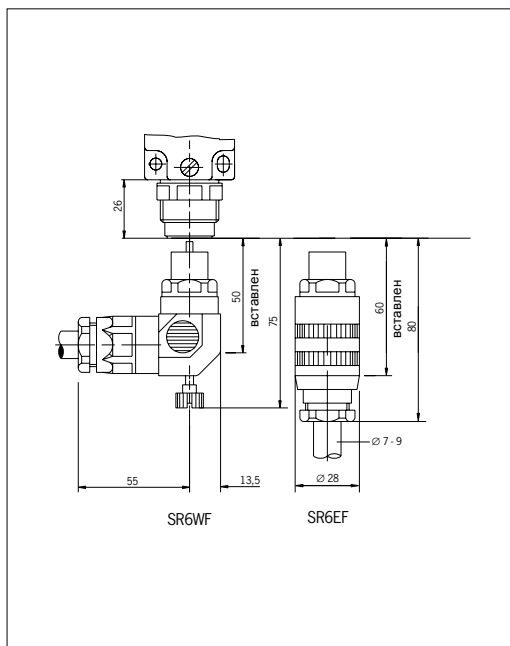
Чертеж с размерами NG2... со штекерным соединителем SR6
